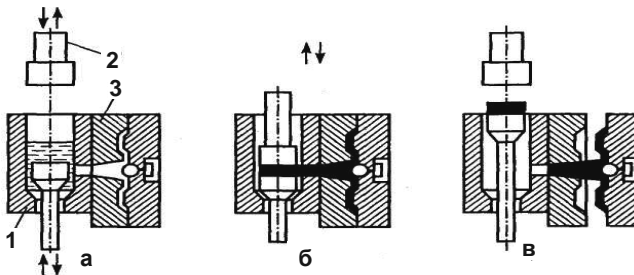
Схеми поршневих машин для лиття під тиском: подавання металу в передкамеру (а); нагнітання металу в робочу порожнину (б); вибивання виливка (в); 1 – передкамера; 2 – поршень; 3 – прес-форма
